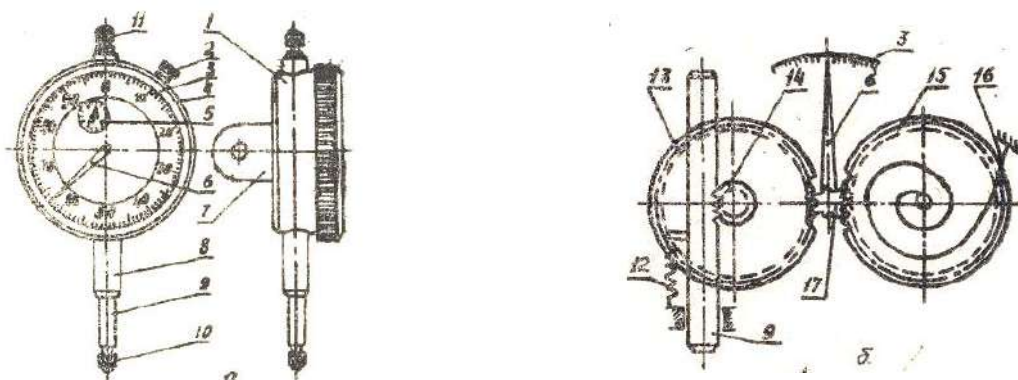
Индикатор типового типа. 1-корпус; 2-стопорный винт; 3-основная шкала; 4-круг; 5-шкала счетчика оборотов; 6-основной большой указатель; 7-ушко; 8 - гильза; 9 - измерительный стержень; 10-наконечник измерительного стержня; 11-псевдоним; 12-возвратная пружина; 13...15, 17-зубчатое колесо; 16-спиральная пружина.
